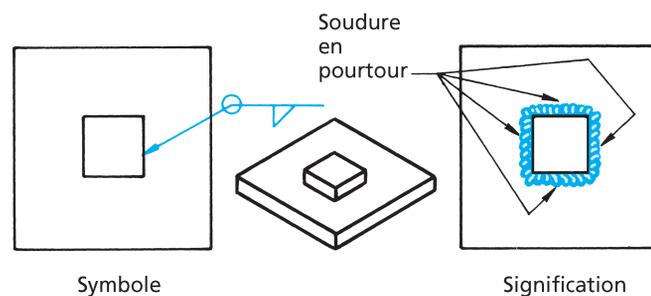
■ Soudure d'angle en pourtour.
